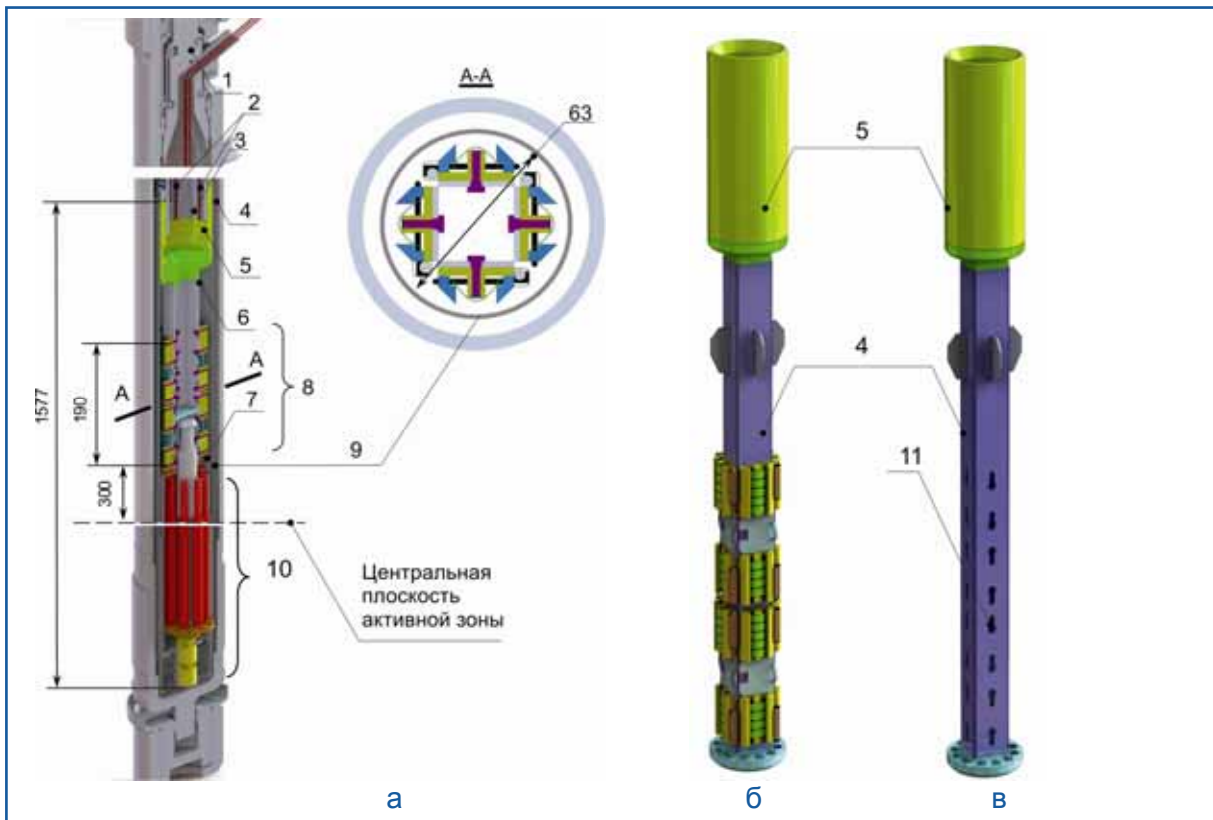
Конструктивные схемы облучательного устройства (а) для испытаний образцов (с поперечным сечением) и его держателя в первом (б) и втором (в) исполнении: 1 — головка петлевого канала; 2 — термоэлектрический преобразователь; 3 — нажимное устройство; 4 — корпус; 5 — головка облучательного устройства; 6 — держатель; 7 — перемешивающая решётка; 8 — пены; 9 — разделитель потока теплоносителя; 10 — подогревный блок; 11 — пазы для установки пены
